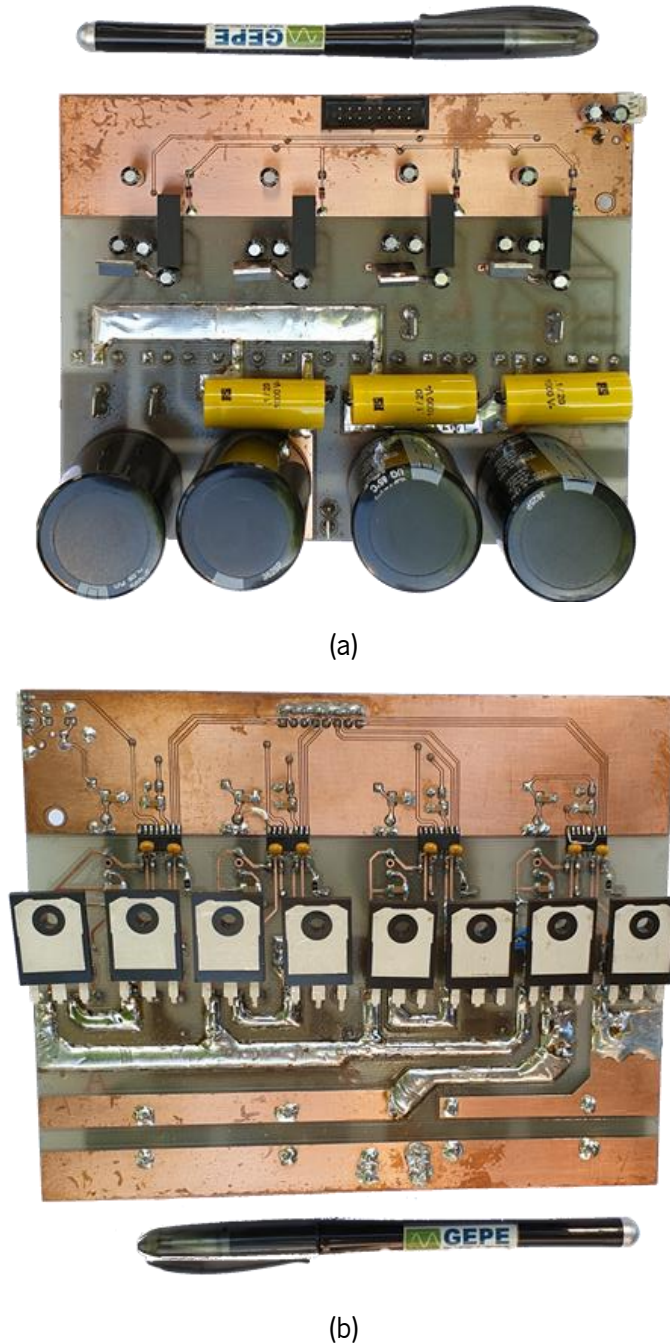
Primeira versão da PCB desenvolvida para o conversor CC-CA: (a) *top* da PCB; (b) *bottom* da PCB.
